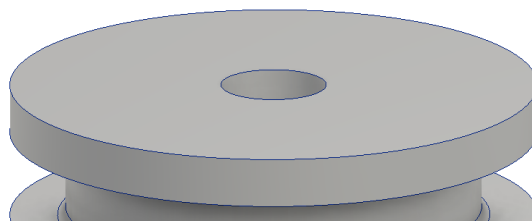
Captura de sección superior de la pieza circular a mecanizar.
